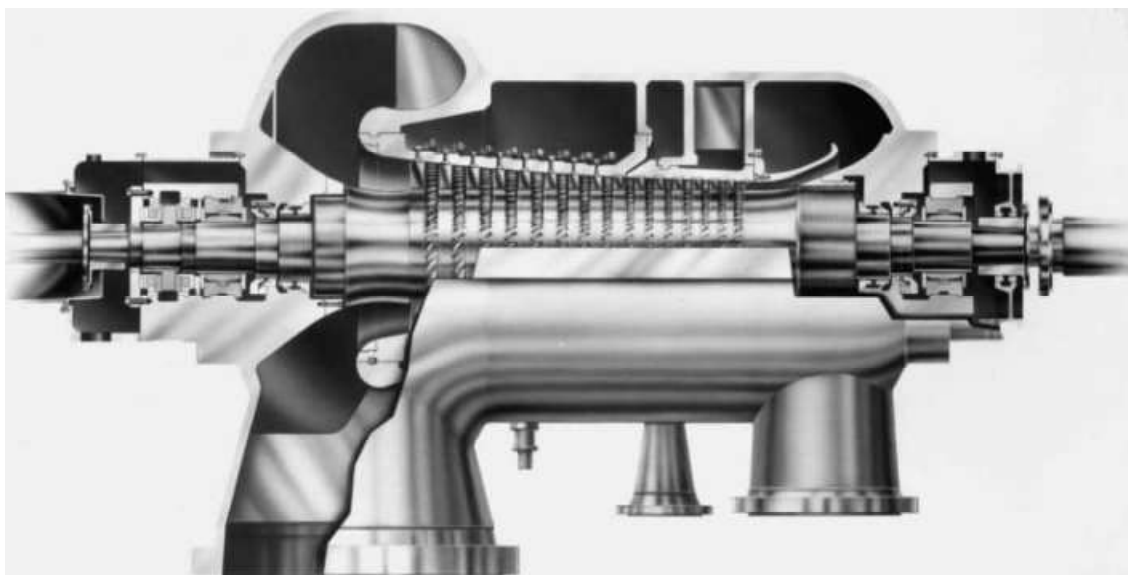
Compressor axial (Fonte: Compressor Hanbook, Paul C. Hanlon)
